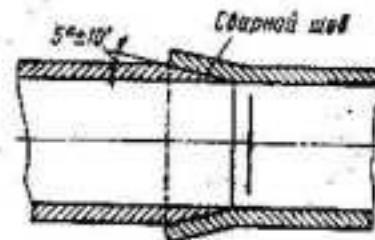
Сварное соединение в конический раструб.
